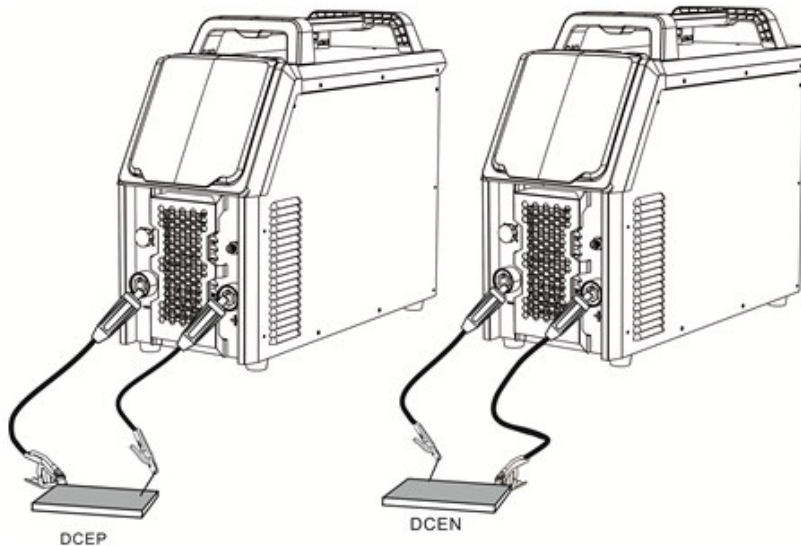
Anschluss und Installation für MMA-Schweißen
